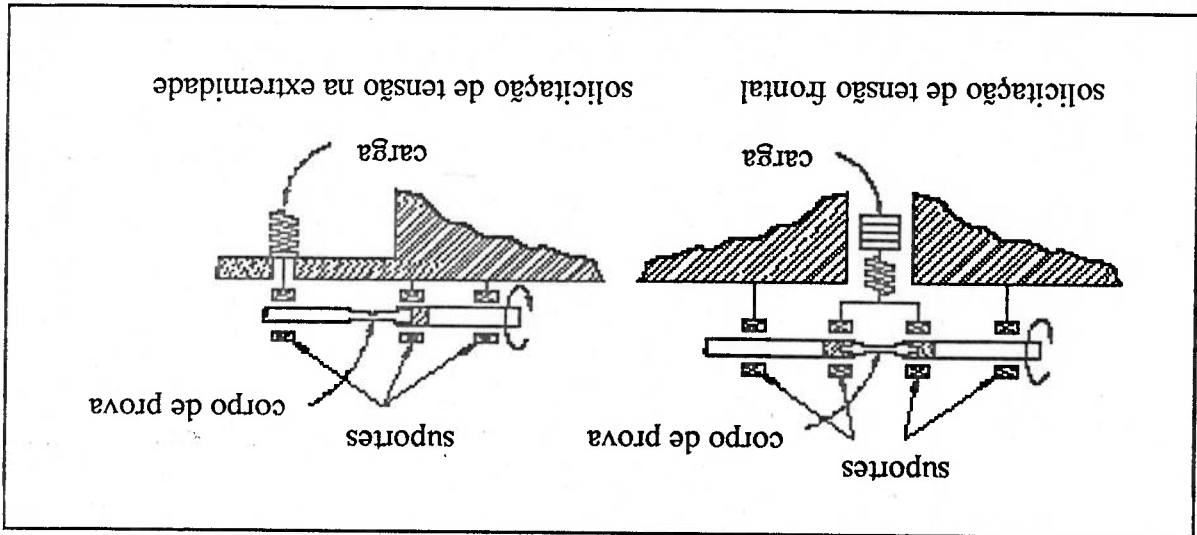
Máquina de Fadiga por Flexão Cíclica de Wöhler
